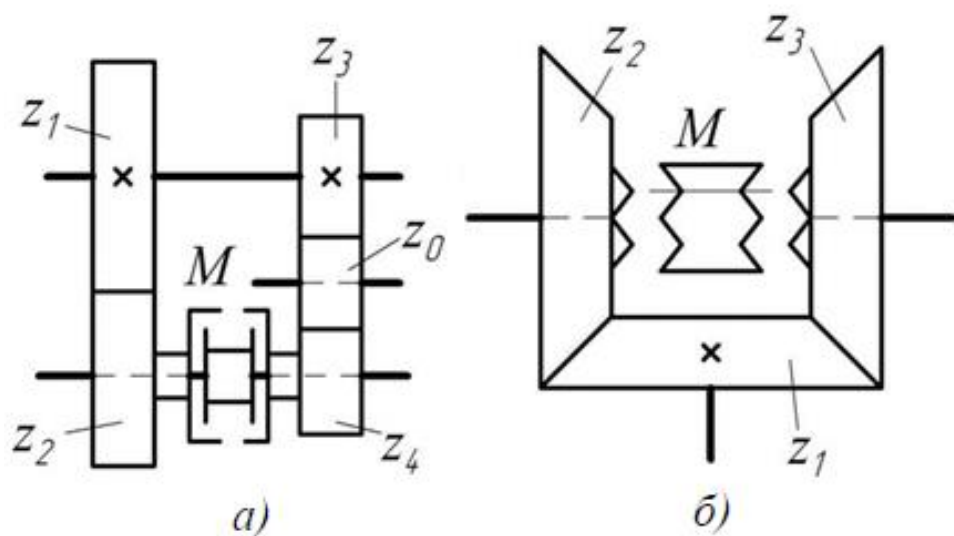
Реверсивні механізми металорізальних верстатів
